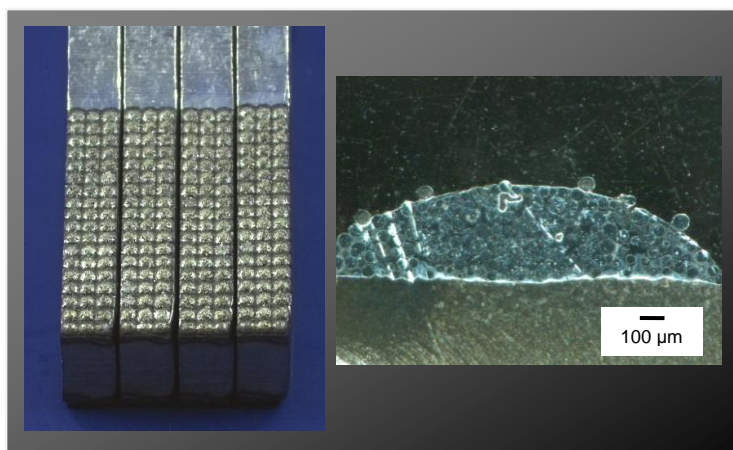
Draufsicht der Punktflächen für strukturierte Gleitschichten (links) Querschliffbild eines Schweißpunktes (rechts)
